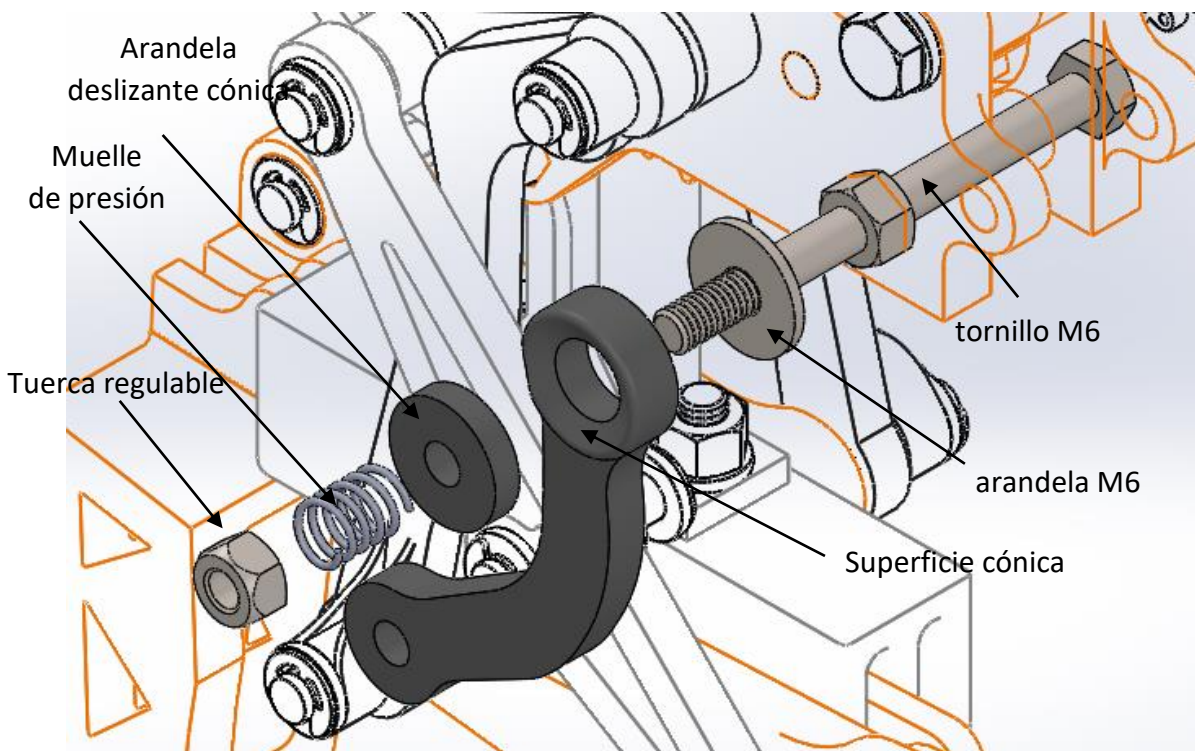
Esquema de vista explosionada del mecanismo excéntrico para adaptación de agarre
